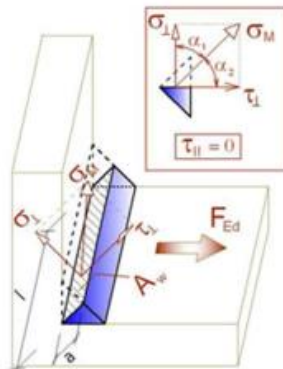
Décomposition des charges de soudure, source [11]
